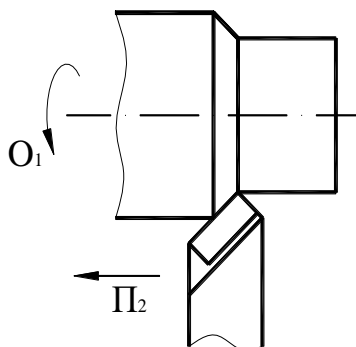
Формоутворення при точінні круглих циліндричних деталей
